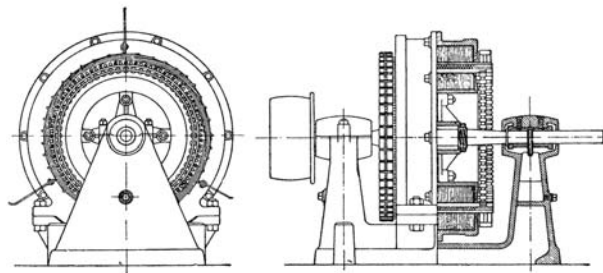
Трехфазный двадцатисильный асинхронный двигатель конструкции Ч. Брауна
